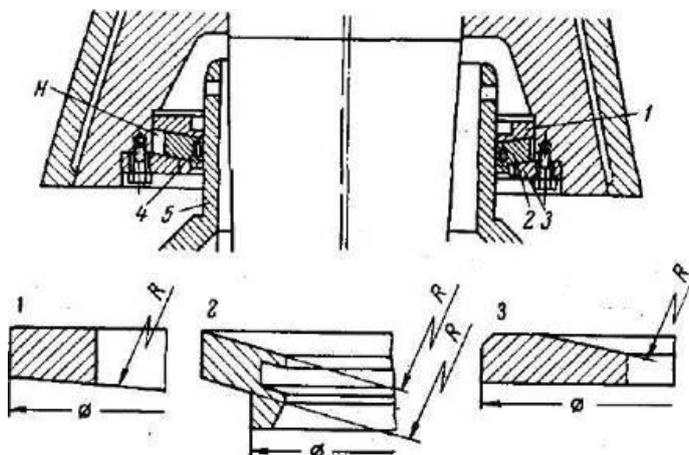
Пылеуплотнение конусной дробилки крупного дробления
